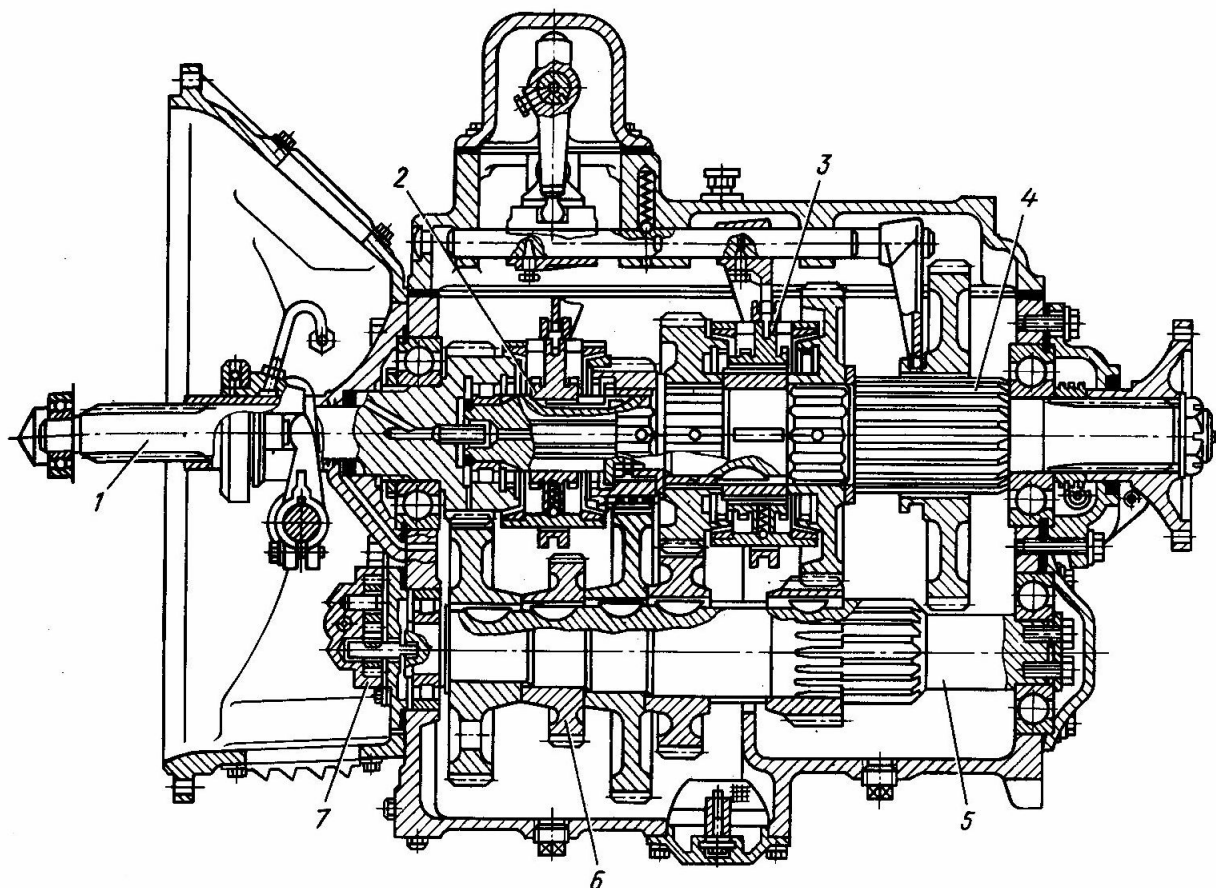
Трехвальная пятиступенчатая коробка передач
